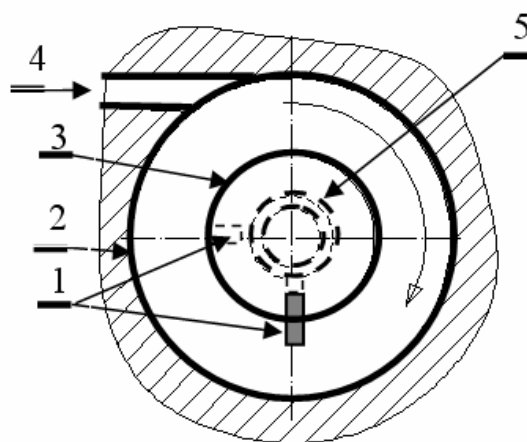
Схема цилиндра вихревой трубы с центральным стержнем переменного сечения
